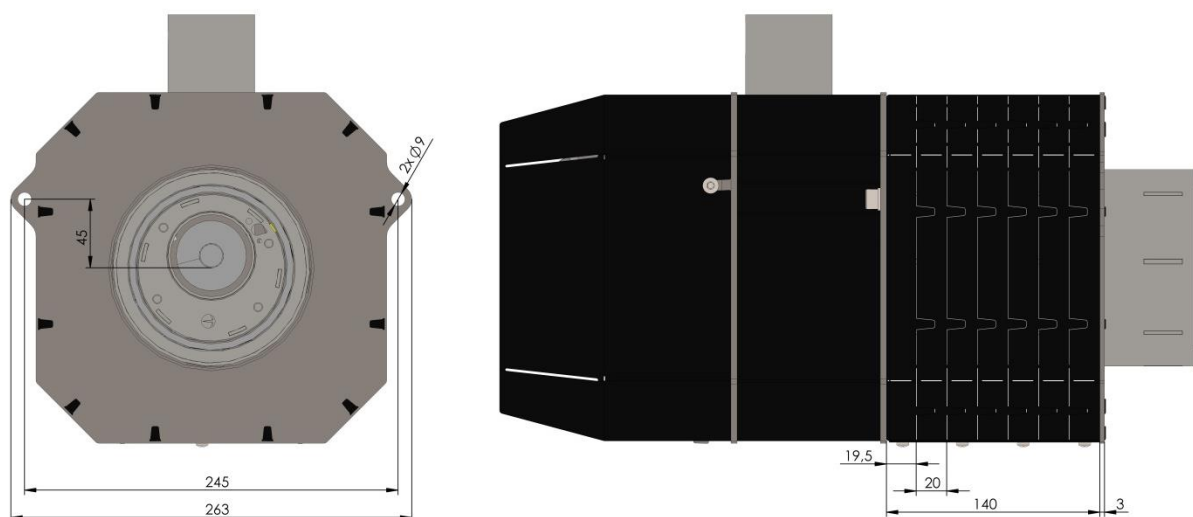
Zobrazení hořáku 5-20 kW s izolačním pláštěm a montážní přírubou
